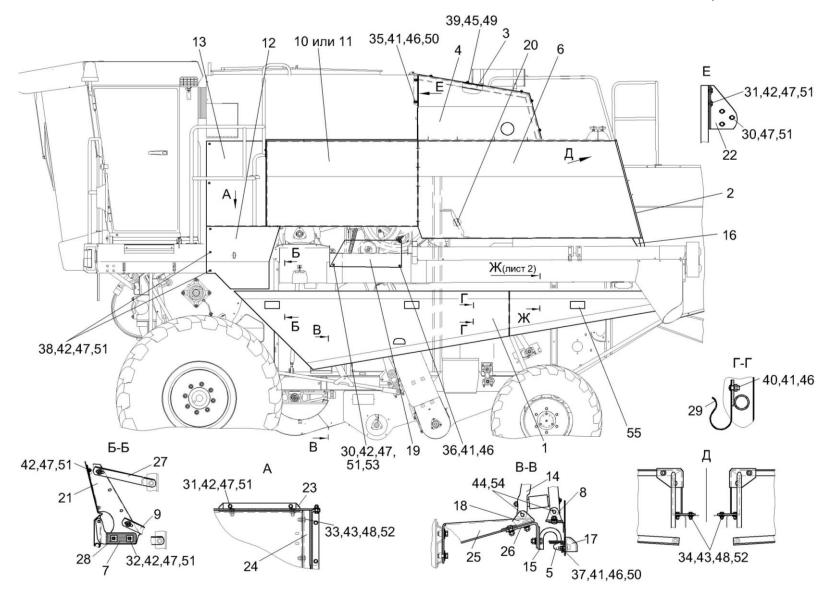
Установка капотов и ограждений КЗК-8А-0128000-02 (лист 1)
